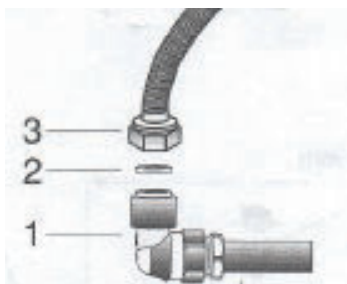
LIGAÇÕES DO TUBO METÁLICO
